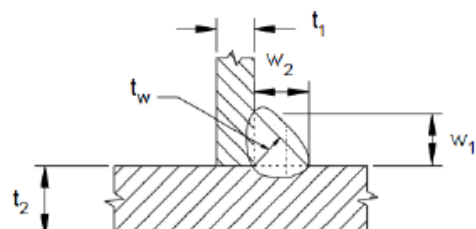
B Soldaduras de filete - Unión en T
